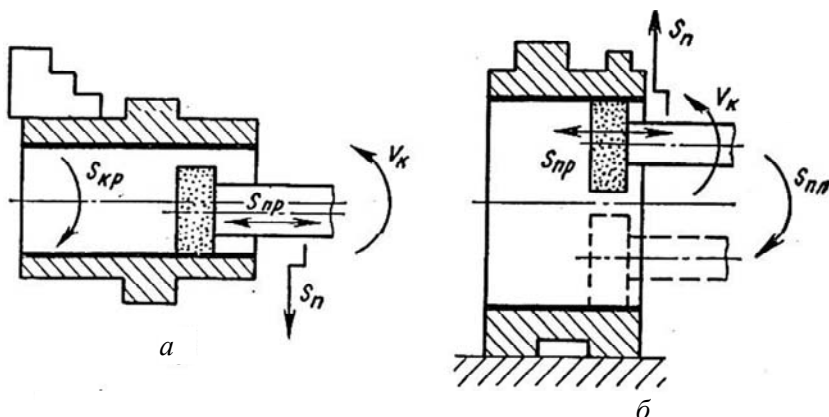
Схема шлифования внутренних цилиндрических поверхностей
